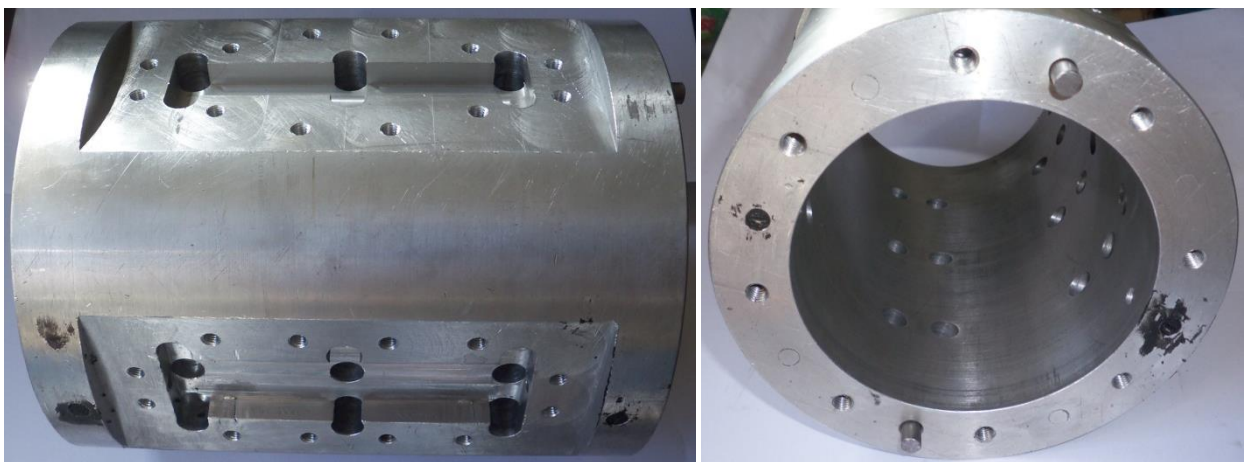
Корпус роторно-поршневого двигателя 12РПД 4,4/1,75
